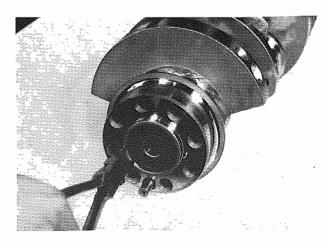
Togliere l'anello di arresto Removing retainer ring
